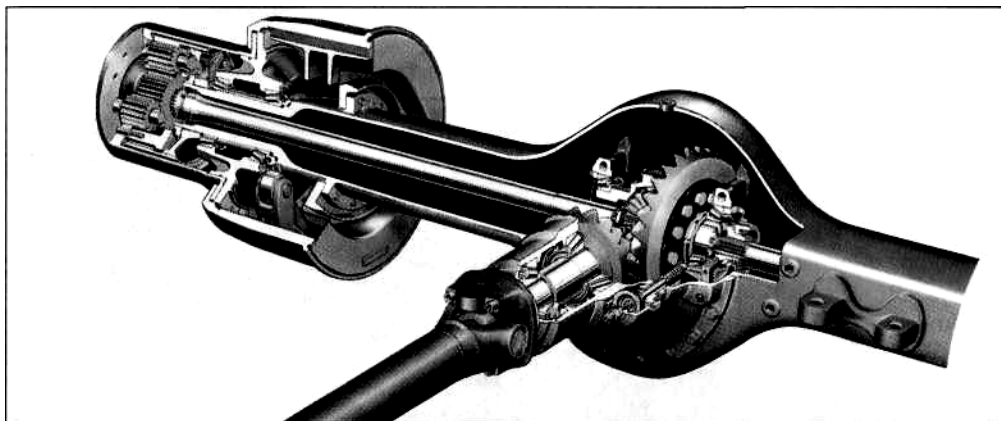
Ведущий мост грузового автомобиля с разнесенной главной передачей и колесными планетарными редукторами
